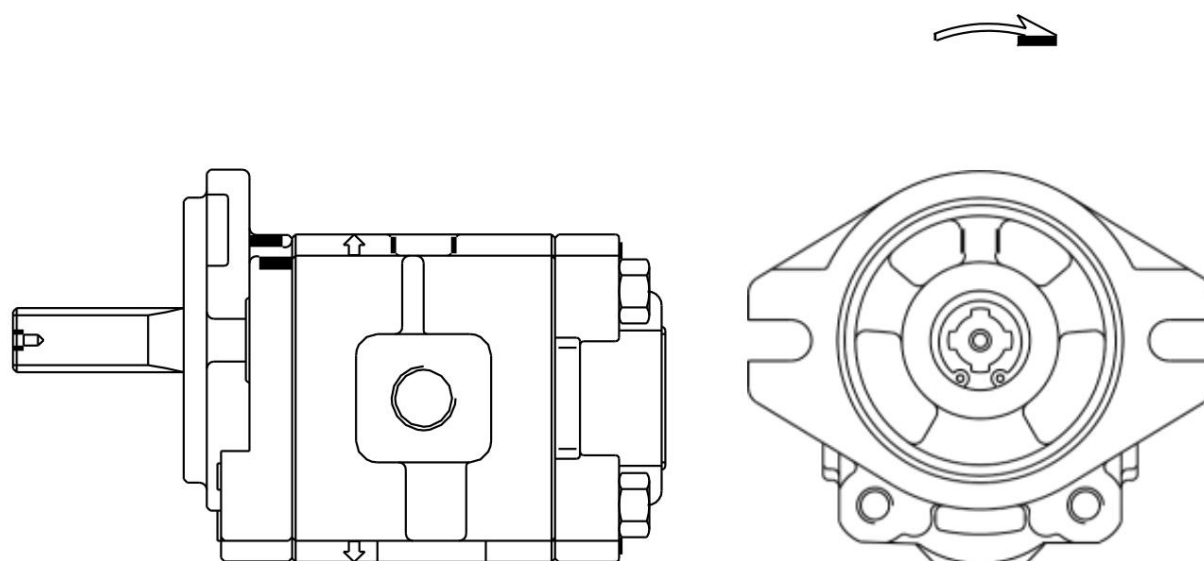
Schéma d'encombrement d'une pompe à engrenages
